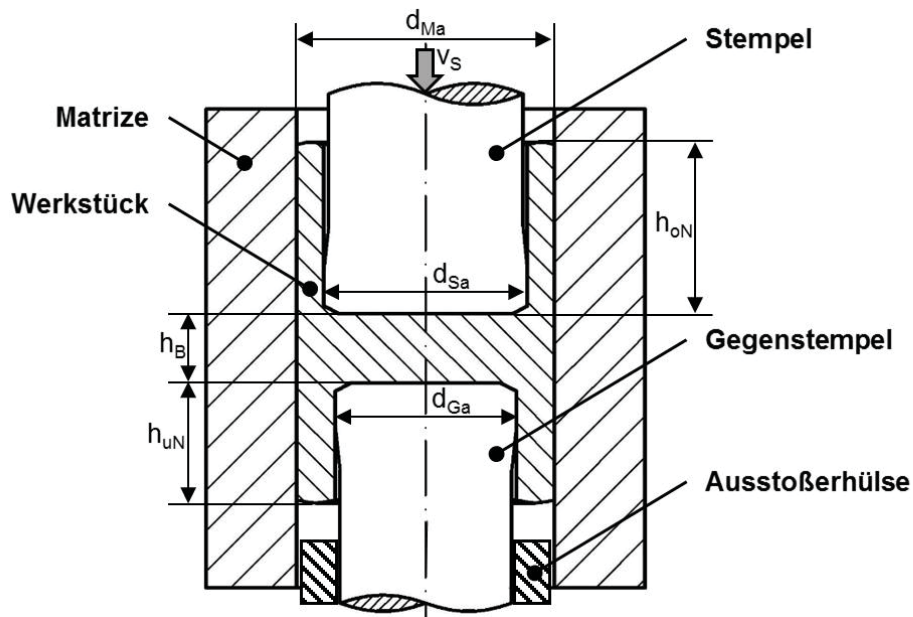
Prinzipskizze des NV-NR-FP mit einem bewegten Werkzeugelement (Stempel)
